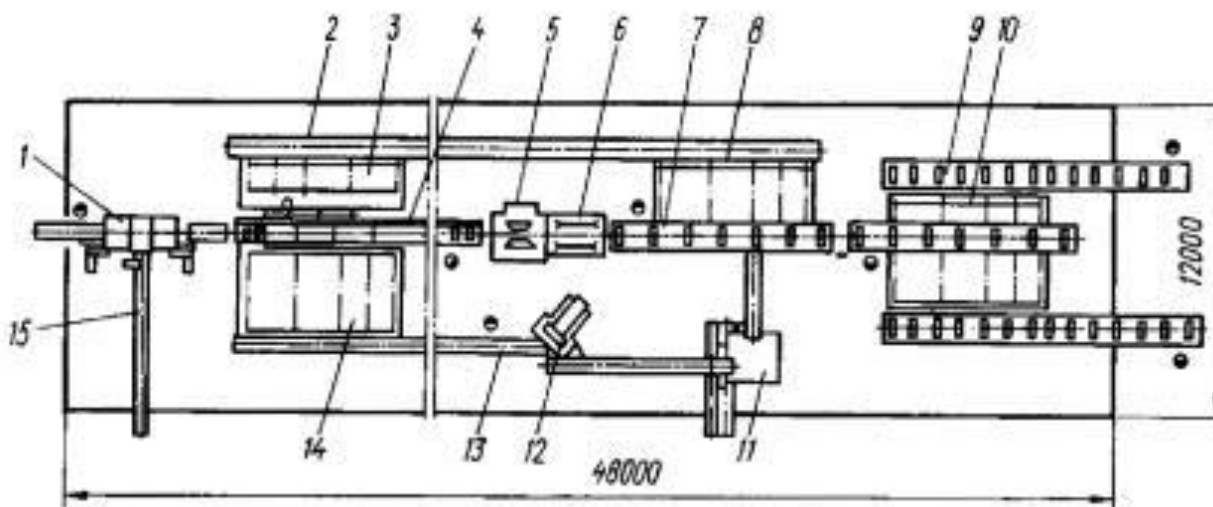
Технологическая схема лесопильного цеха с головным фрезерно- брусующим станком для обработки тонкомерного сырья
